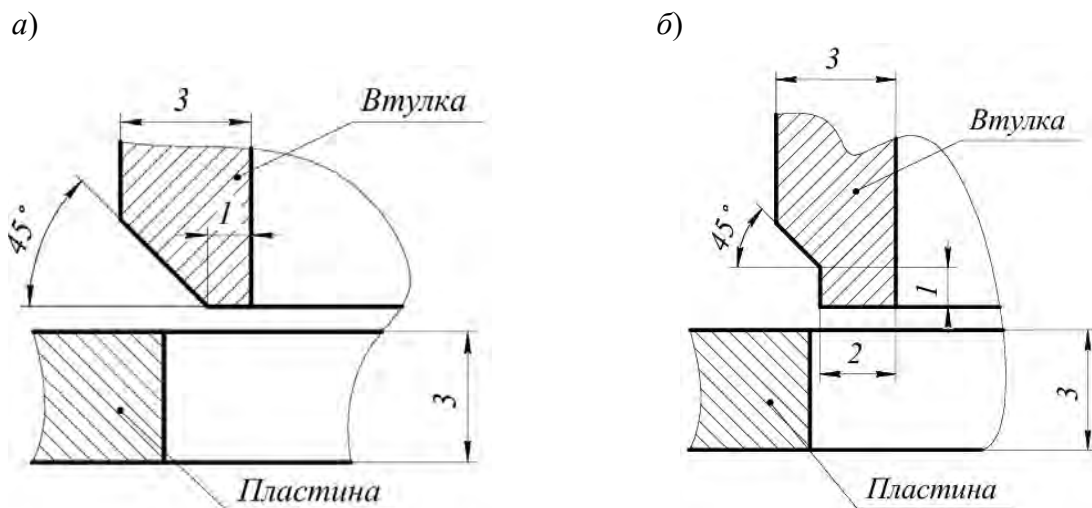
Размеры рельефов на торце втулки конической (а) и конической с заступом (б) формы
